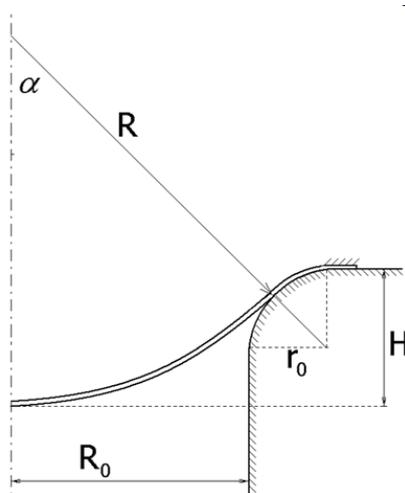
Схема формообразования листа заготовки в цилиндрическую матрицу
